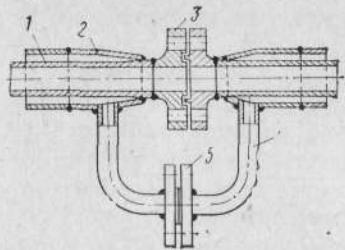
Узел фланцевого соединения трубопровода с рубашкой
